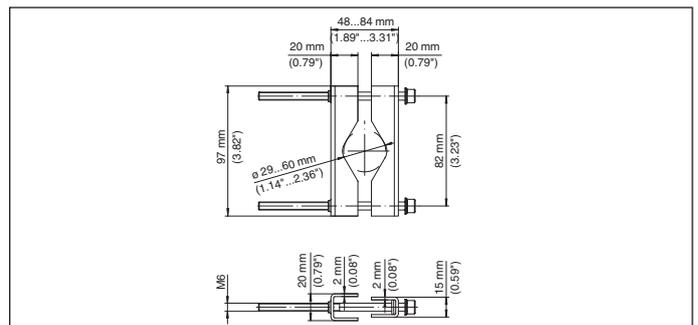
Dimensions équerres pour le montage sur tuyauterie VEGAMET 861, 862
